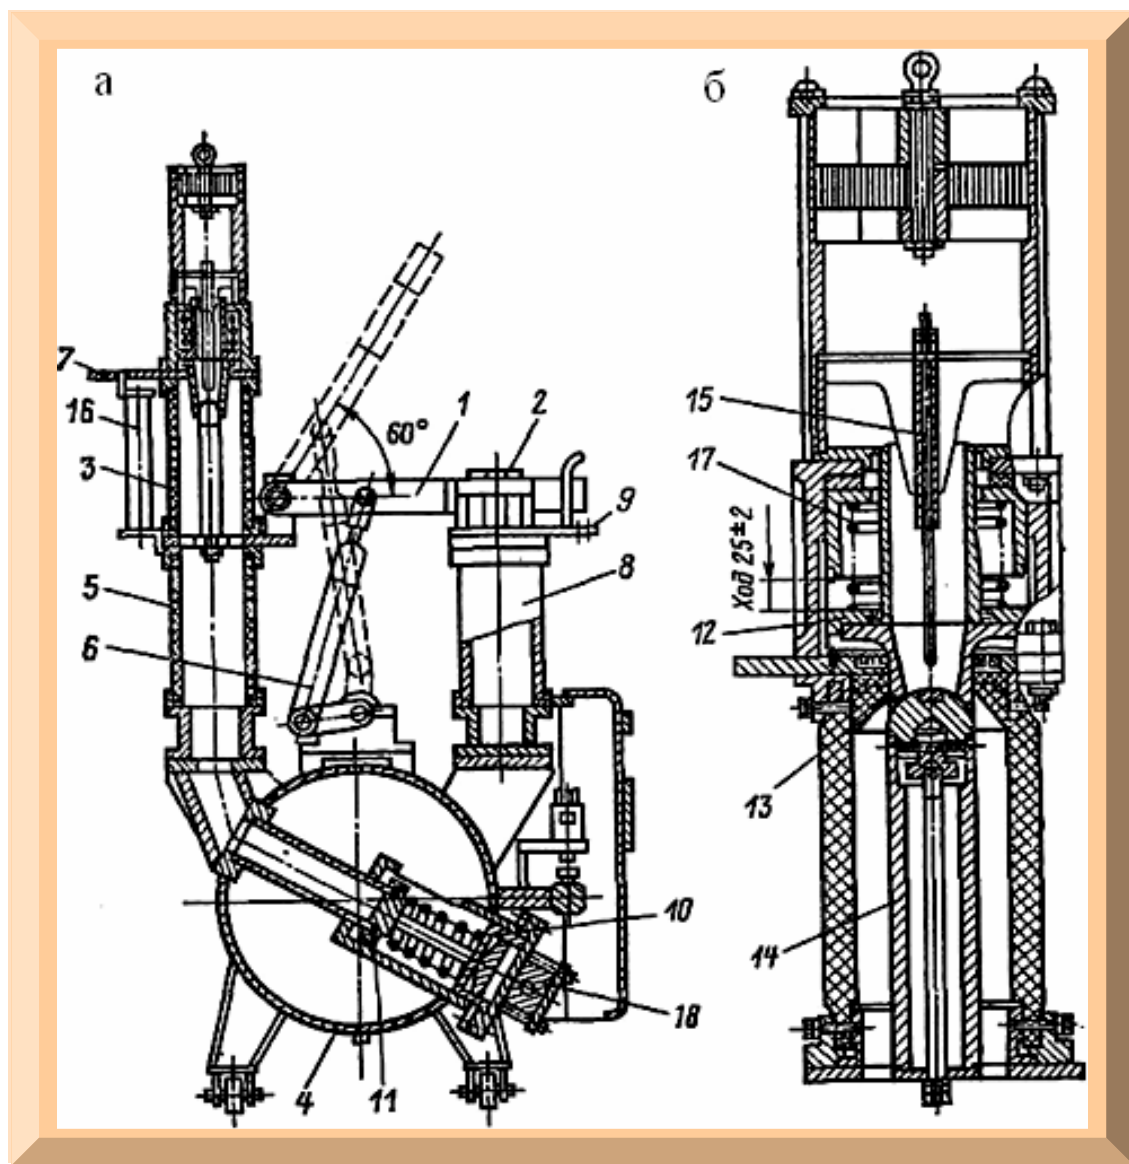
Выключатель ВВП-35: а - общий вид выключателя типа ВВП-35;
